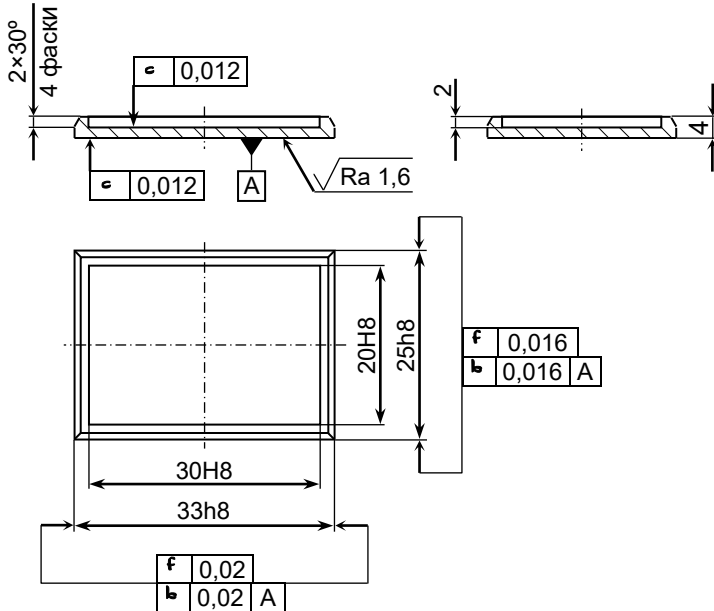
Пример выполнения рабочего чертежа детали «Корпус»
